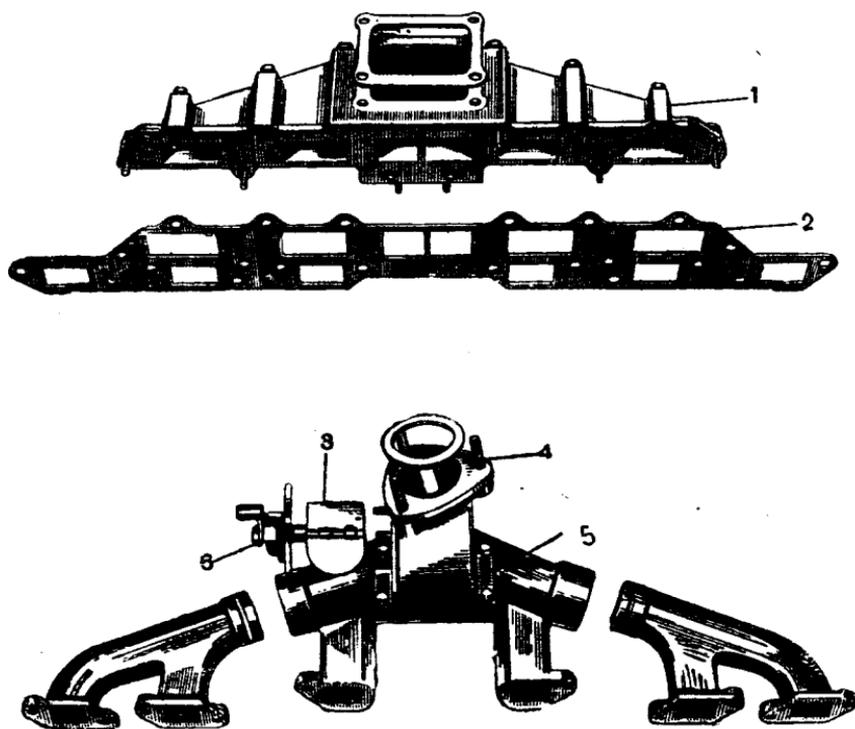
Всасывающий коллектор и выхлопной сборник:
